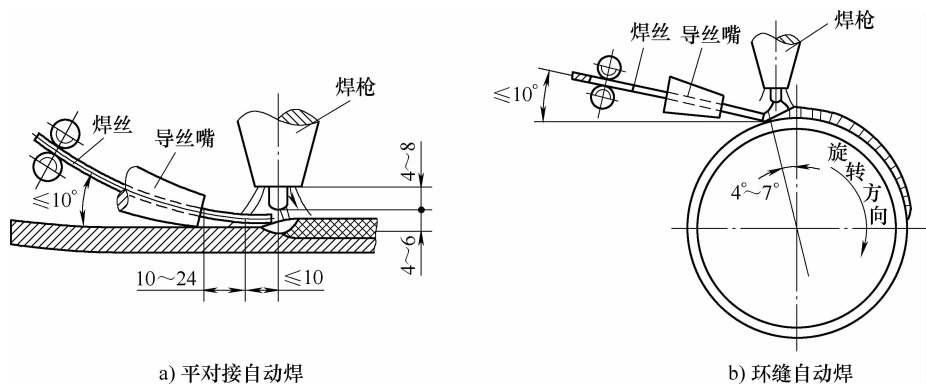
自动送丝 TIG 焊置焊枪焊丝和工件的相对位置图
